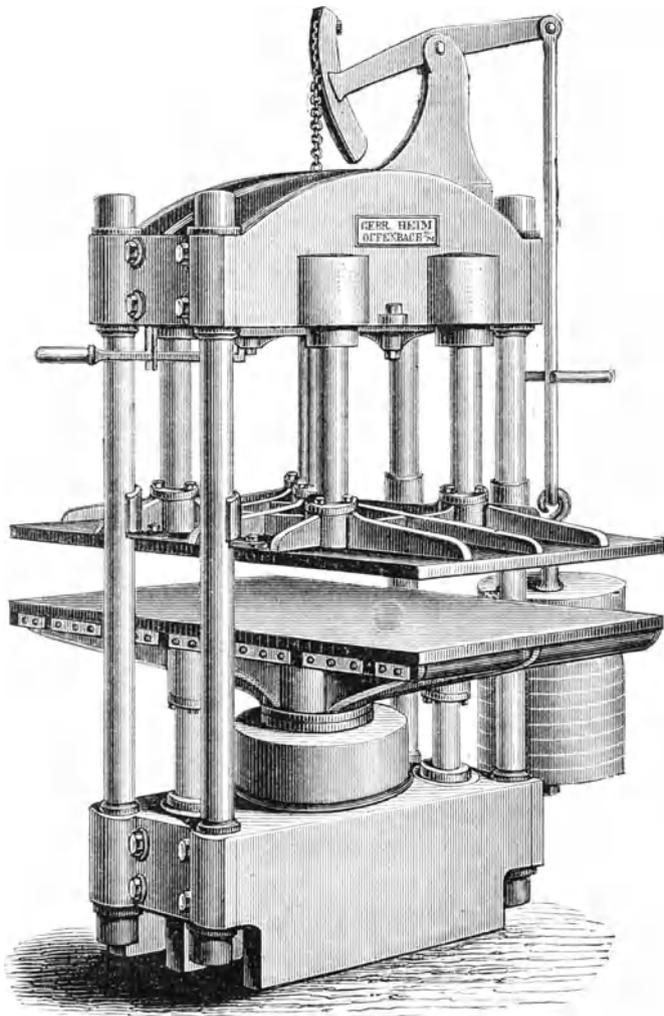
Hydraulische Presse für Farben- und Golddruck auf Zeuge und Stoffe.
